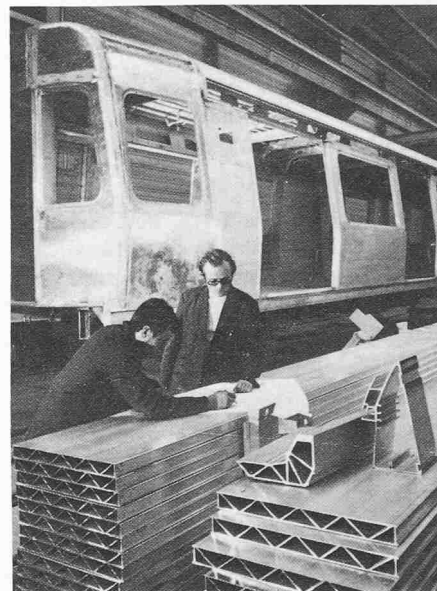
Metro Paris: Typische Hohlkammerprofile für Bodenkonstruktion und Dachgurt
